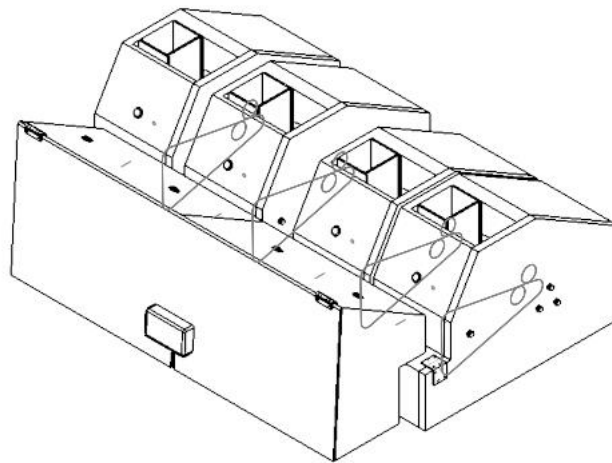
Vista isométrica de la máquina desemblistadora modular.
